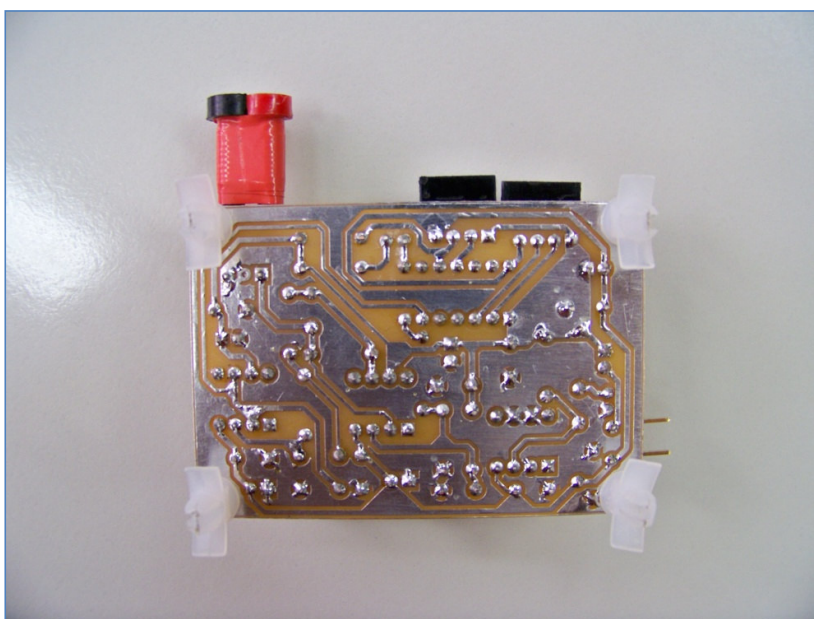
Placa com componentes soldados parte inferior.
